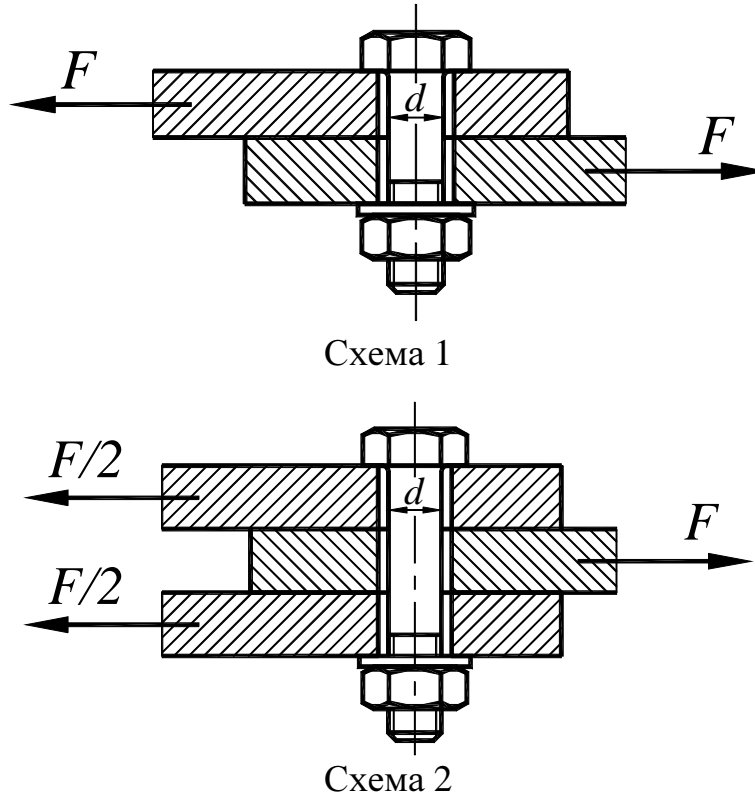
Розрахункові схеми болтового з'єднання із зазором
